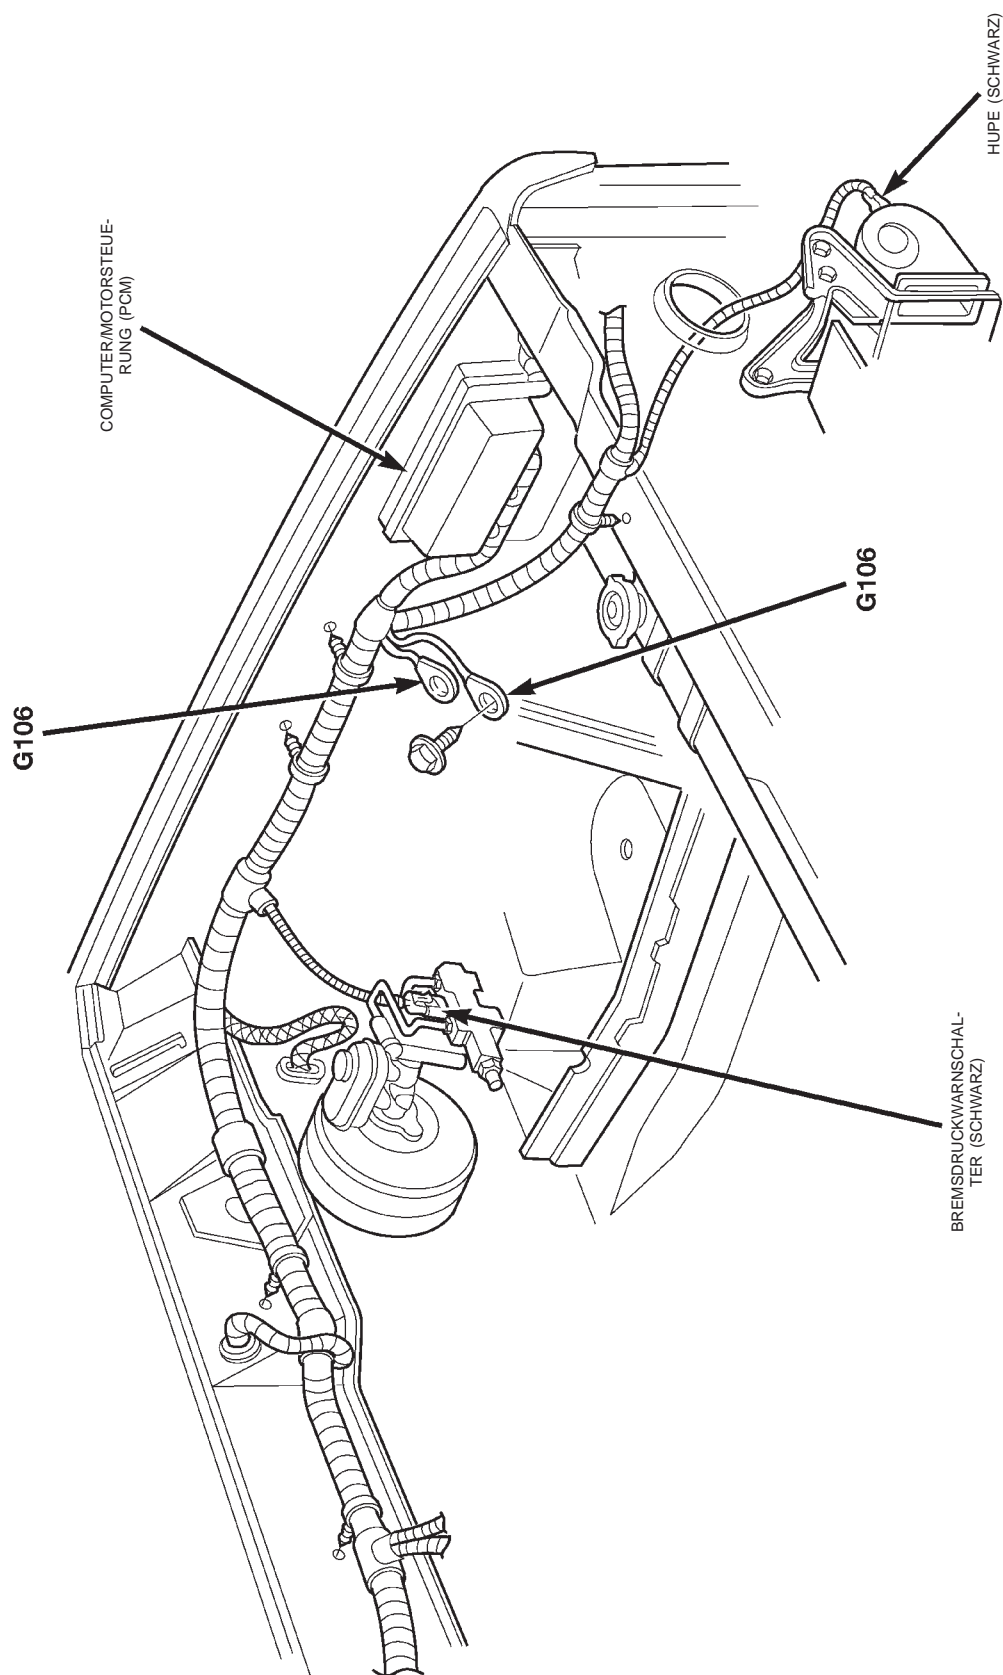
Motorraum links 2.5L-Motor Linkslenker
